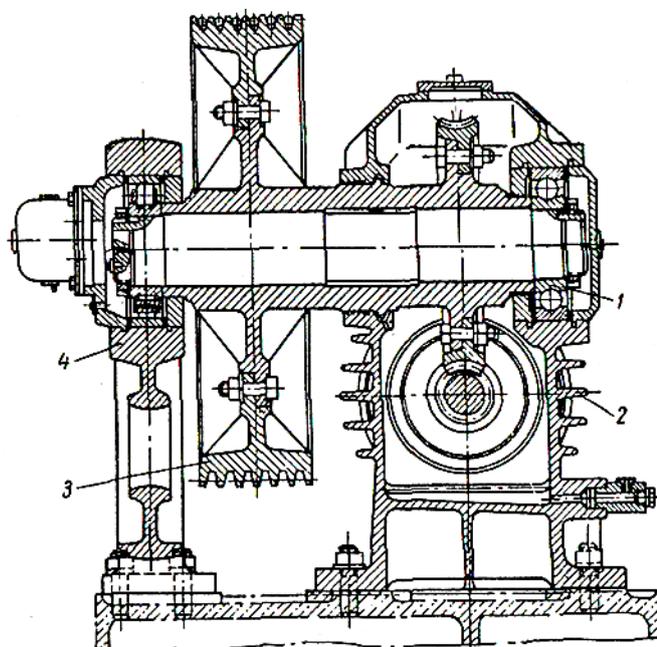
Узел вала червячного колеса редукторной лебедки
